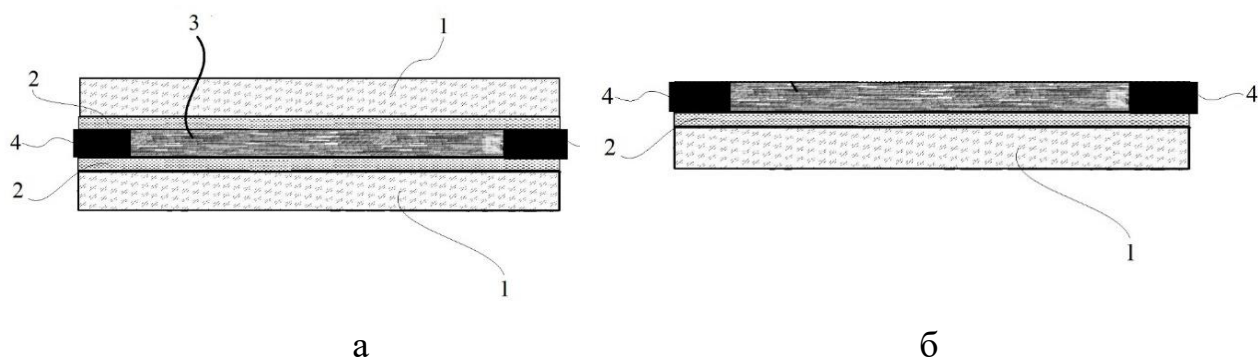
Схема сборки лабораторного образца эластичного полимерного композита: а) двухслойного, б) однослойного
